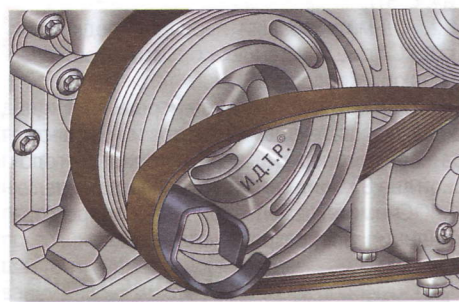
Установка ремня привода компрессора кондиционера на приспособление для его монтажа
